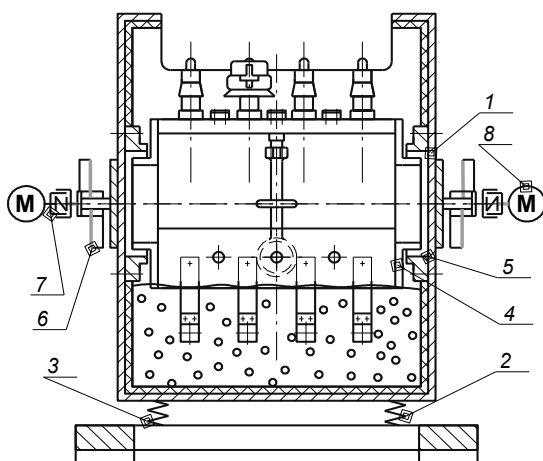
Конструктивна схема машини з обертним пристроєм для обробки деталей
